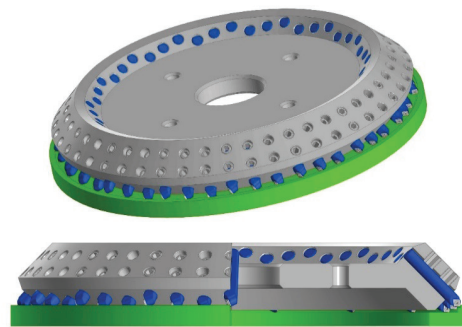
3D-модель наструюваної триступінчастої торцевої фрези та наструювального калібру-кільця
